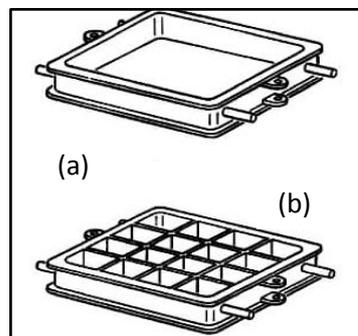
Châssis pour moulage main, (a) châssis simple, (b) châssis à barres pour gros moulage (en fonte ou en acier soude)[6]
